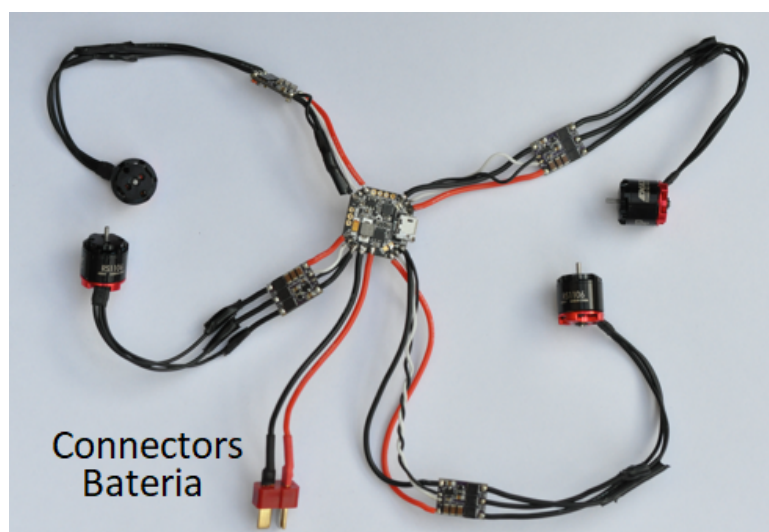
Resultat de la soldadura dels quatre motors i del cablejat de la bateria a la controladora.
